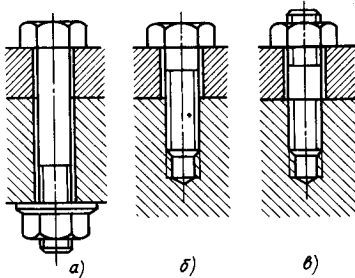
Основные типы резьбовых крепежных деталей: а — болт; б — винт; в — резьбовая шпилька
